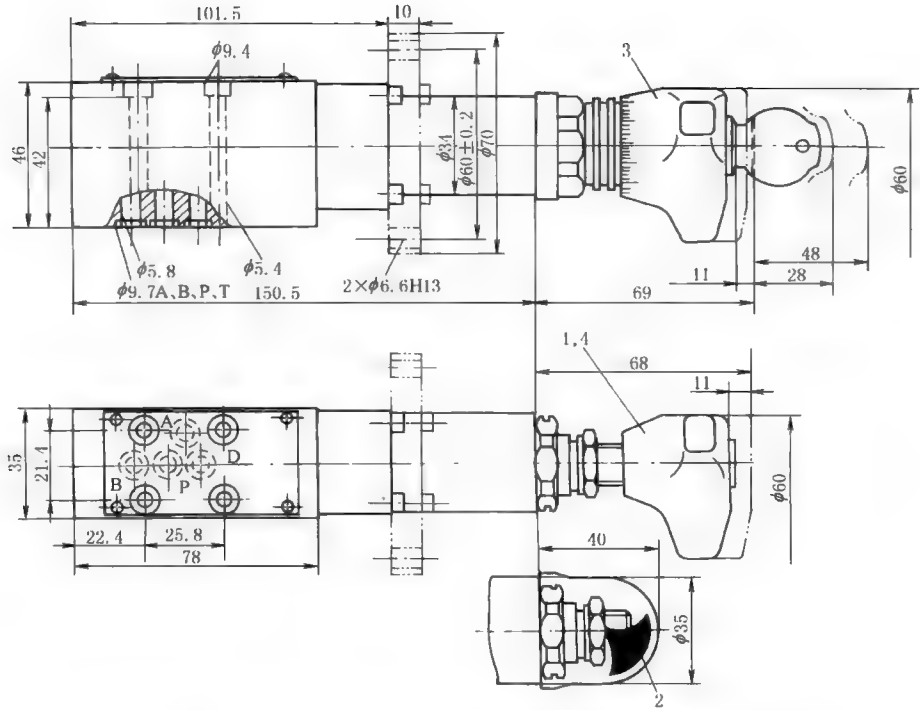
DZ5DP 型直动式顺序阀外形尺寸
